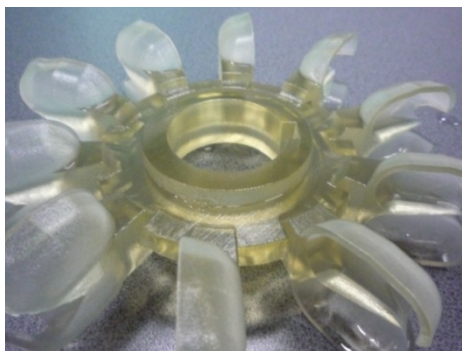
Rotorul turbinei Pelton după operațiile de postprocesare, fabricat în cadrul laboratorului de Tehnologii integrate de fabricație al Universității Transilvania din Brașov [27]
